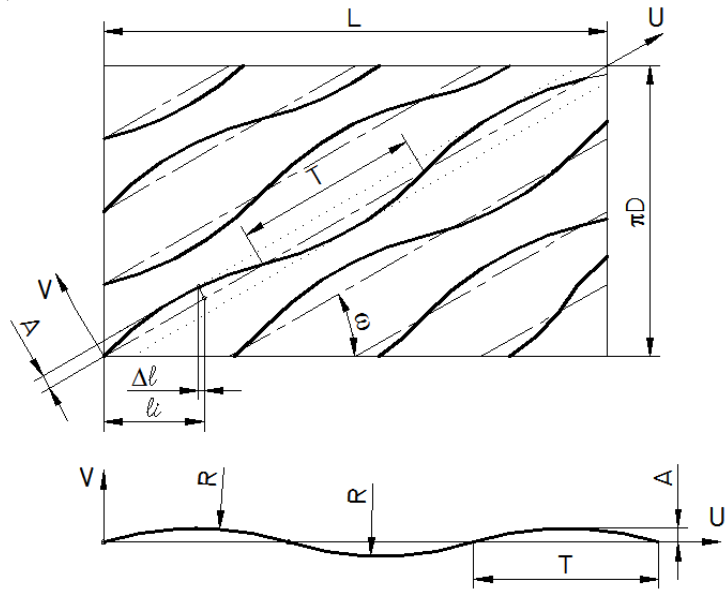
Развертка концевой фрезы с волнистой режущей кромкой
